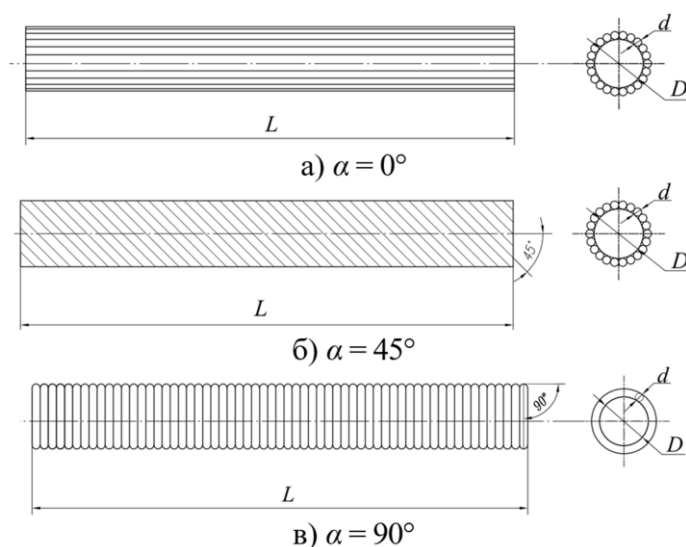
Схемы расположения упрочнённых волокон на поверхности цилиндрических заготовок
